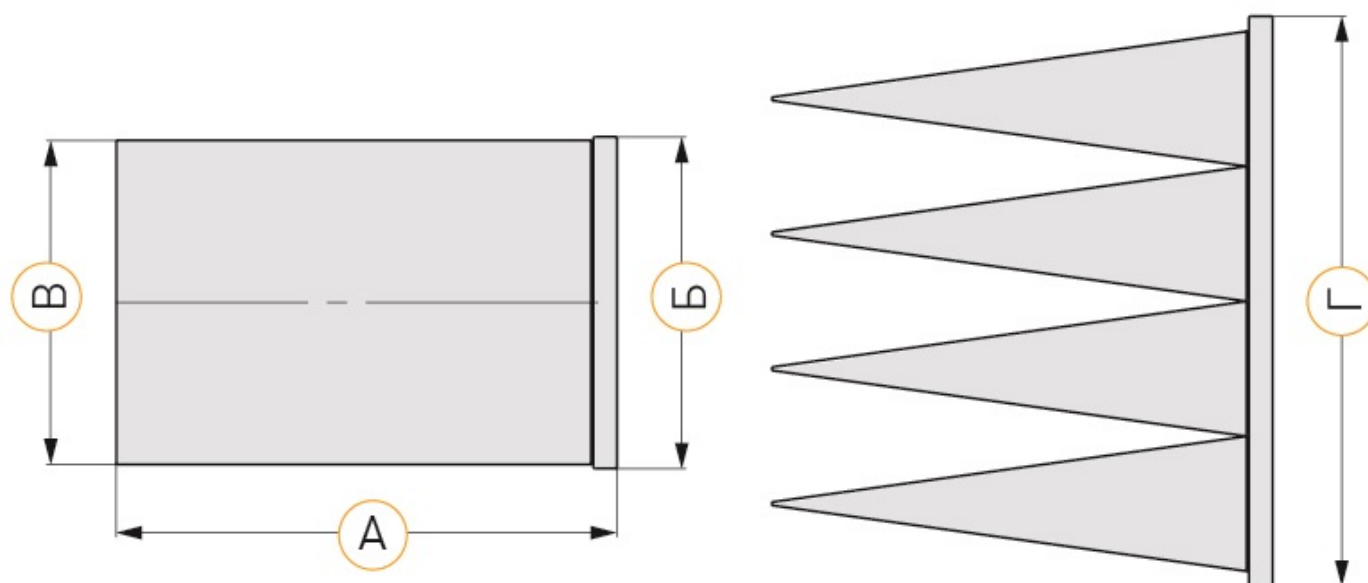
Внешний вид и основные размеры фильтрующих вставок SPU
